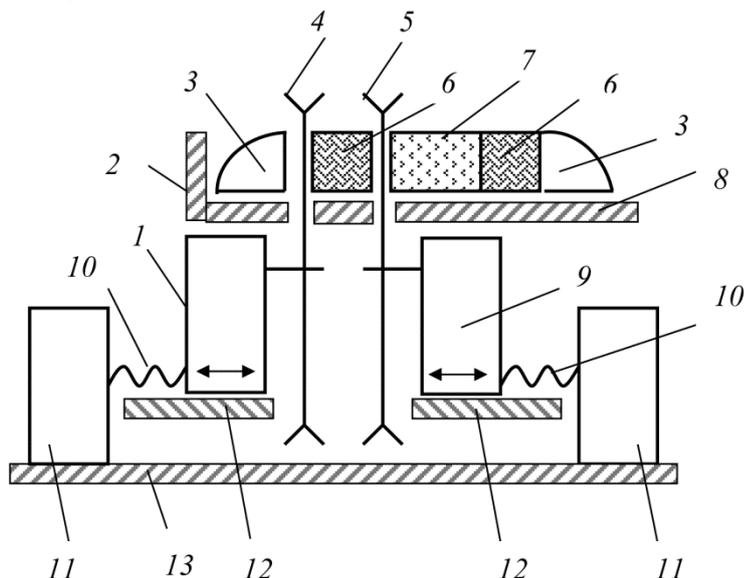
Схема переработки древесины с ядровой гнилью на обрезном станке: 1, 9 – электродвигатели; 2 – боковые направляющие; 3 – обзоленные кромки обрезаемого пиломатериала; 4, 5 – дисковые пилы для выпиливания обзоленной кромки и здоровой древесины; 6 – полосы здоровой древесины; 7 – ядровая гниль; 8 – горизонтальные направляющие; 10 – винтовая подача; 11 – устройства для смещения электродвигателей; 12 – направляющие; 13 – станина
